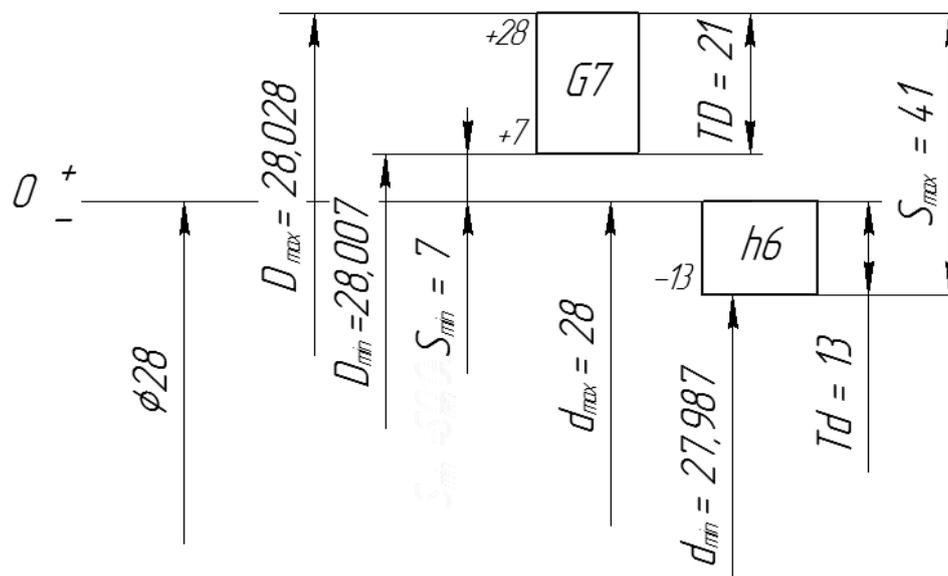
Схема расположения полей допусков посадки с зазором
